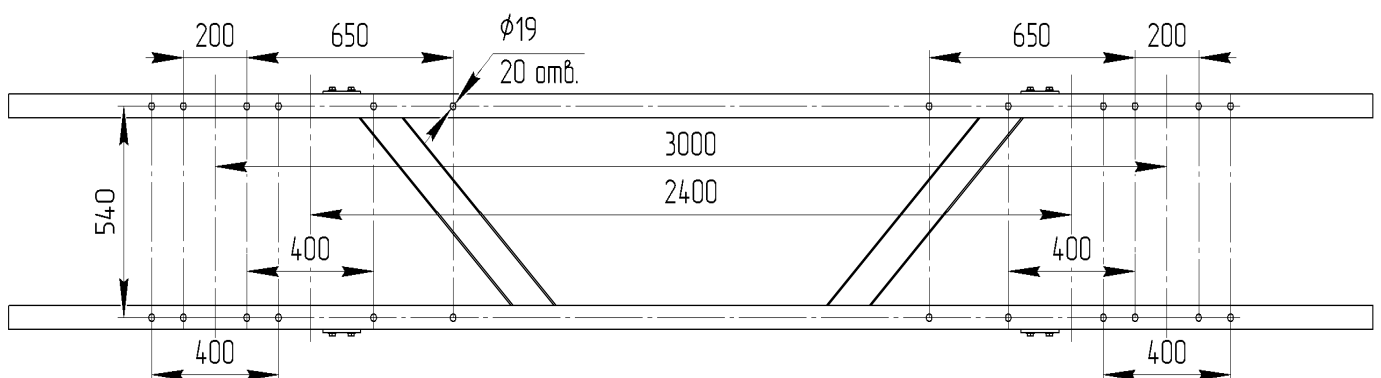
Разметка отверстий на общей раме для крепления на опорную конструкцию
